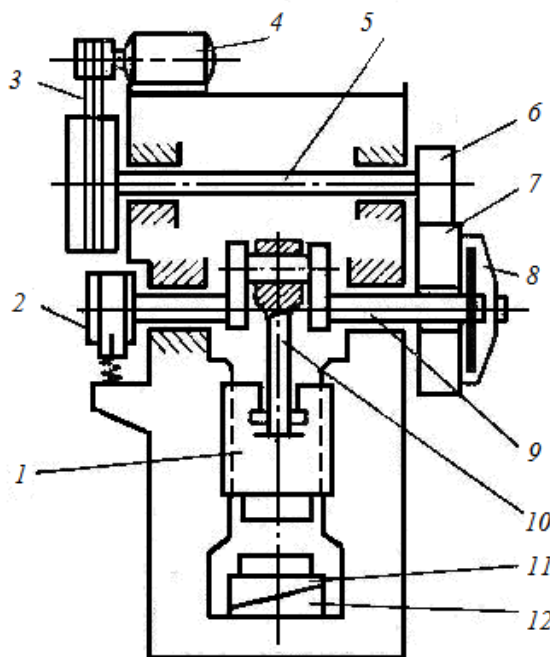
Кінематична схема кривошипного гарячештампувального преса: 1 – повзун; 2 – гальмо; 3 – шків з маховиком, з'єднані клинопасовою передачею; 4 – двигун; 5 – проміжний вал; 6 – шестерня, що знаходиться в зачепленні із зубчастим колесом 7; 8 – багатодискова фрикційна муфта; 9 – колінчастий вал; 10 – шатун; 11 – штамп; 12 – стіл штампового преса
